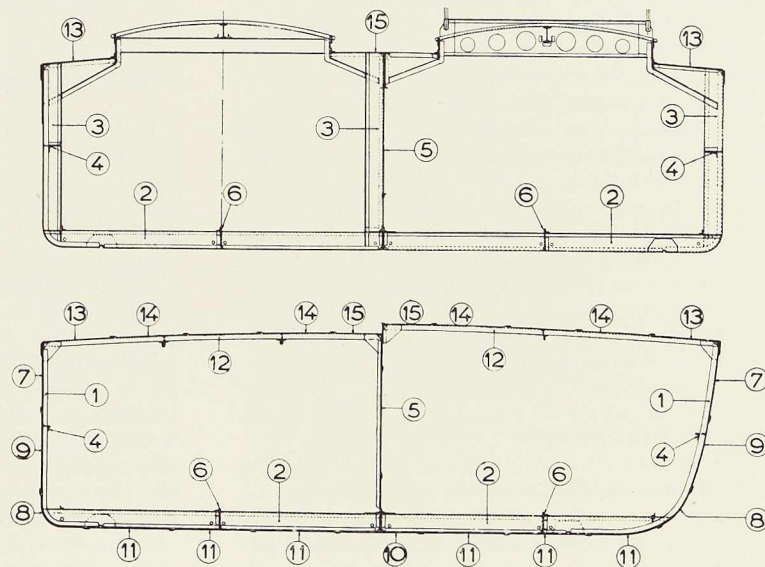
En haut à gauche : coupe barrots mobiles n° 38. En haut à droite : coupe barrots mobiles n° 67. En bas à gauche : coupe n° 52. En bas à droite : coupe n° 18. Les chiffres entourés d'un rond renvoient au paragraphe « Détails de construction » de la page 248.
